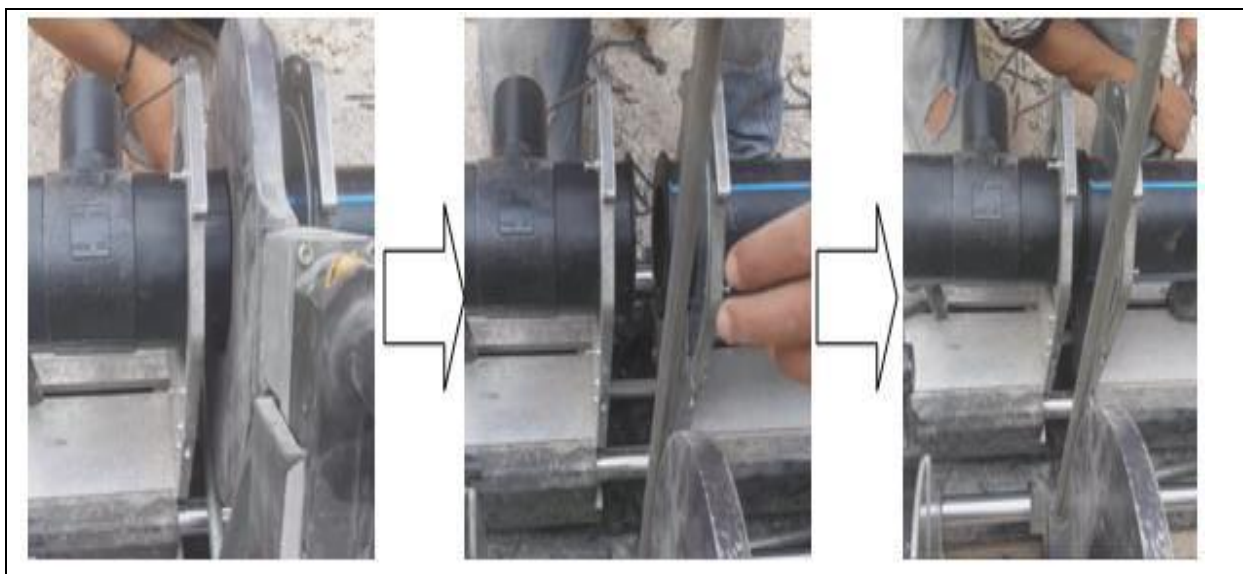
chauffage des tubes lors du soudage bout à bout
